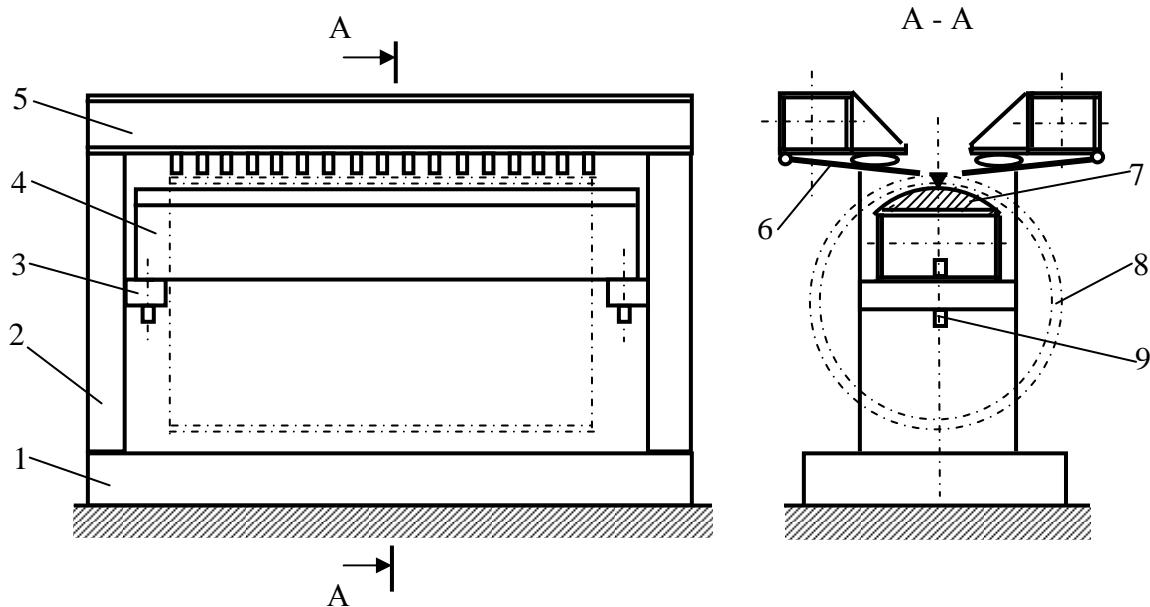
Схема станда для складання та зварювання поздовжніх швів обичайок: 1 - рама; 2 - стояк; 3 - кронштейн; 4 - нижня опорна балка; 5 - верхня опорна балка; 6 - клавішний притискач з пневмошланговим приводом; 7 - металева підкладка; 8 - обичайка; 9 - шворінь;
